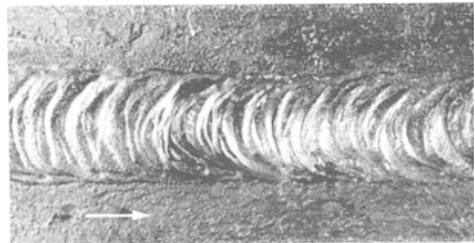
Schweißnaht an 10 mm-Stahlblech (Nachrechtsschweißung).
